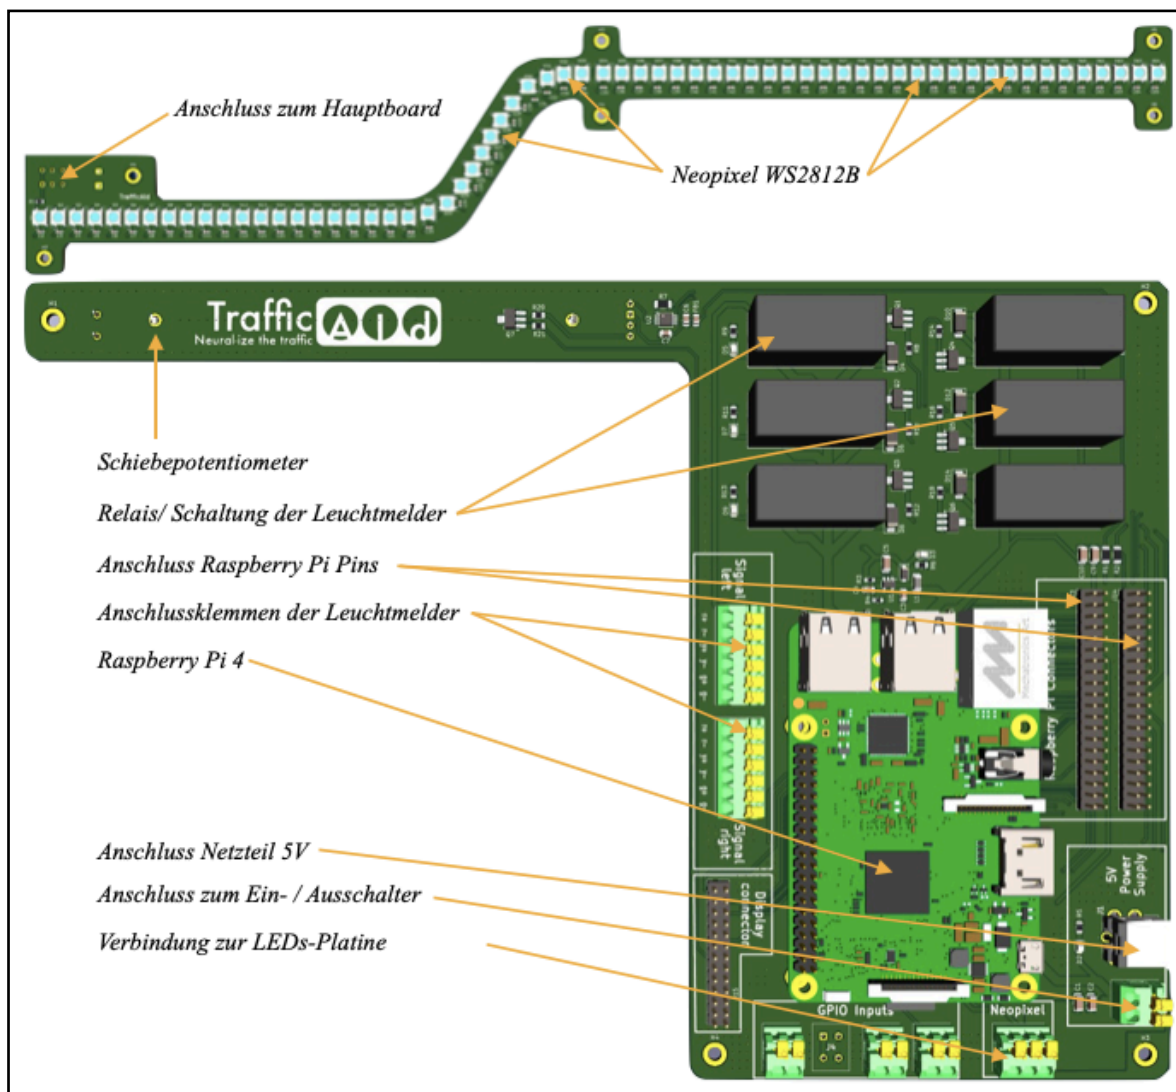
3D-Darstellung der Platinen mit Bauteilen. Erstellt mit KiCad.
